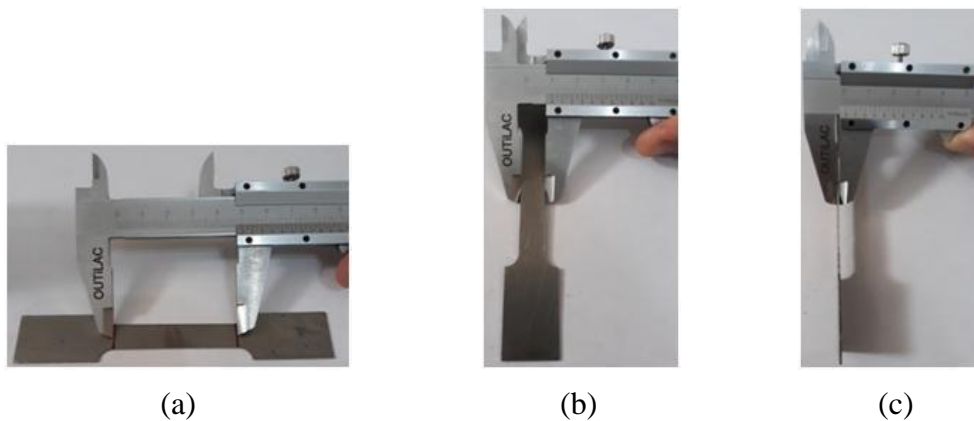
Vérification des dimensions de la partie utile de l'éprouvette.
